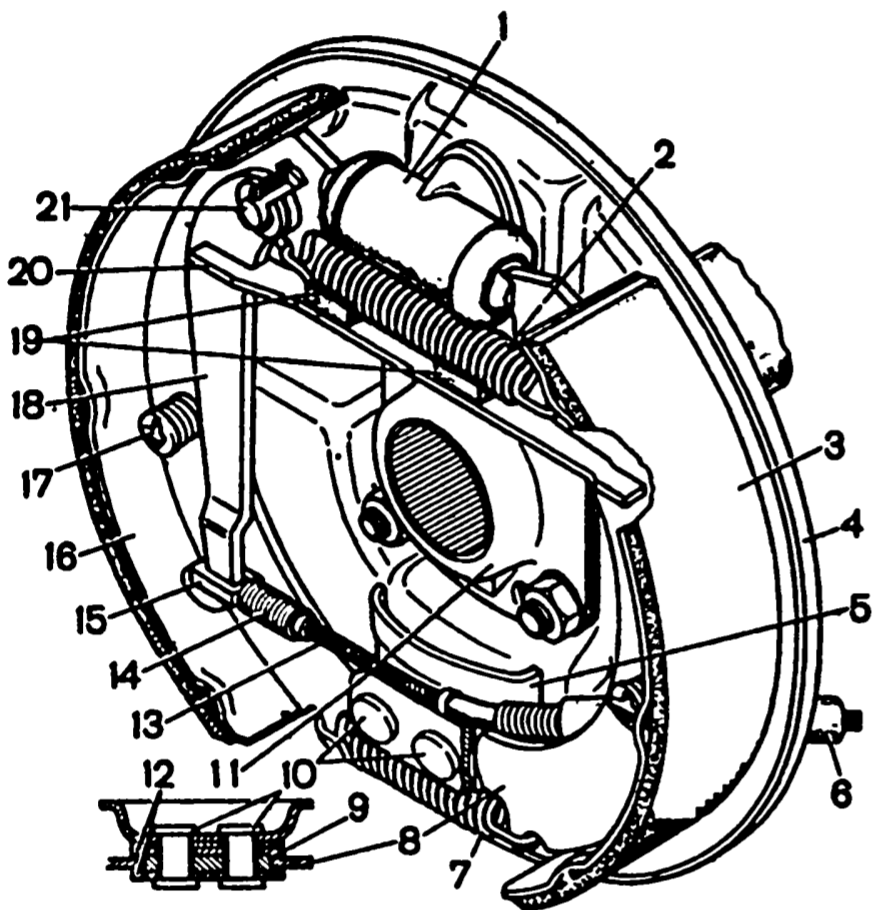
Тормозной механизм заднего колеса: 1 - колесный цилиндр; 2 - верхняя стяжная пружина колодок; 3 - накладка колодки; 4 - щит тормоза; 5 - внутренняя пластина; 6 - оболочка заднего троса; 7 - нижняя стяжная пружина колодок; 8 - передняя тормозная колодка; 9 - опорная пластина колодок; 10 - заклепки; 11 - маслоотражатель; 12 - направляющая пластина колодок; 13 - задний трос стояночного тормоза; 14 - пружина заднего троса; 15 - наконечник заднего троса; 16 - задняя тормозная колодка; 17 - опорная стойка колодки; 18 - рычаг ручного привода колодок; 19 - резиновые подушки; 20 - распорная планка колодок; 21 - палец рычага ручного привода колодок
